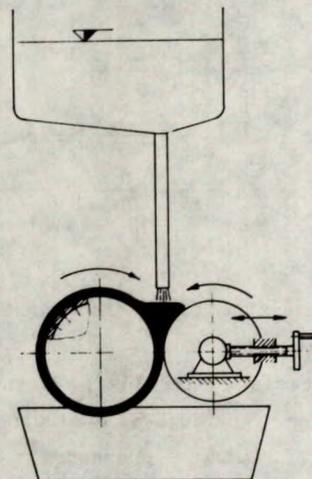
Coupe d'une machine Magnani de fabrication de tuyaux (5)
